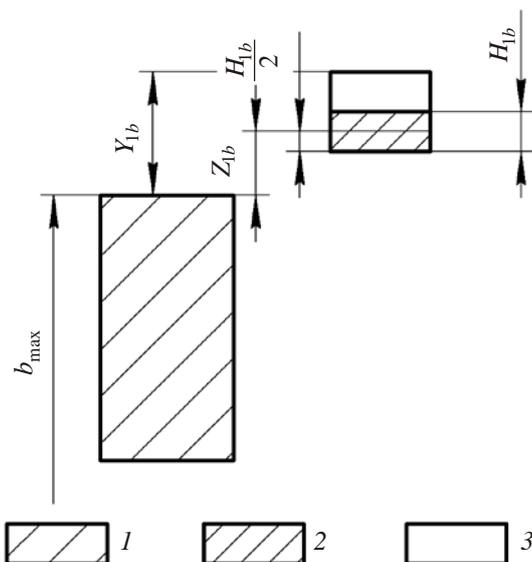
Схема расположения поля допуска калибра-кольца по размеру b вала:
